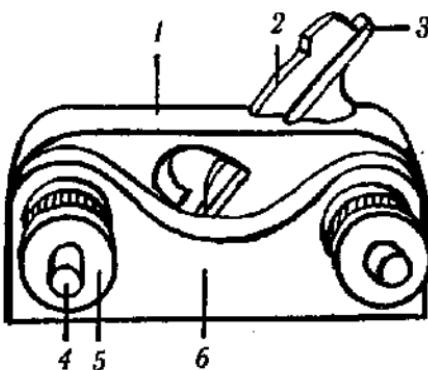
Деревянный шпунтубель: 1 — основная колодка; 2 — клин; 3 — нож, 4 — винт, 5 — гайка; 6 — упорная планка.
